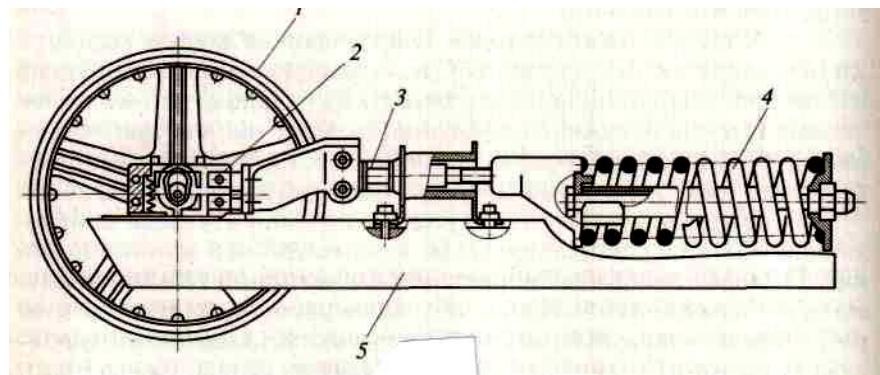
Схема установки направляющего колеса на ползуне:
